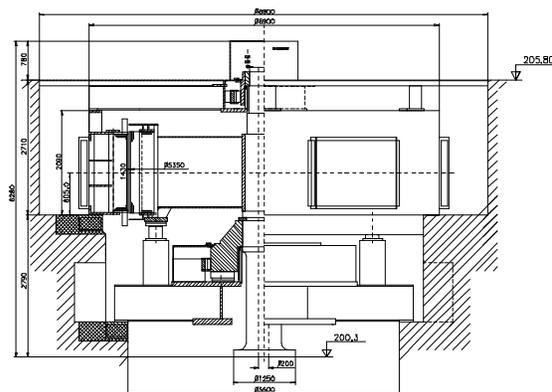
DIMENSIONAL COM MANCAL STANDARD
